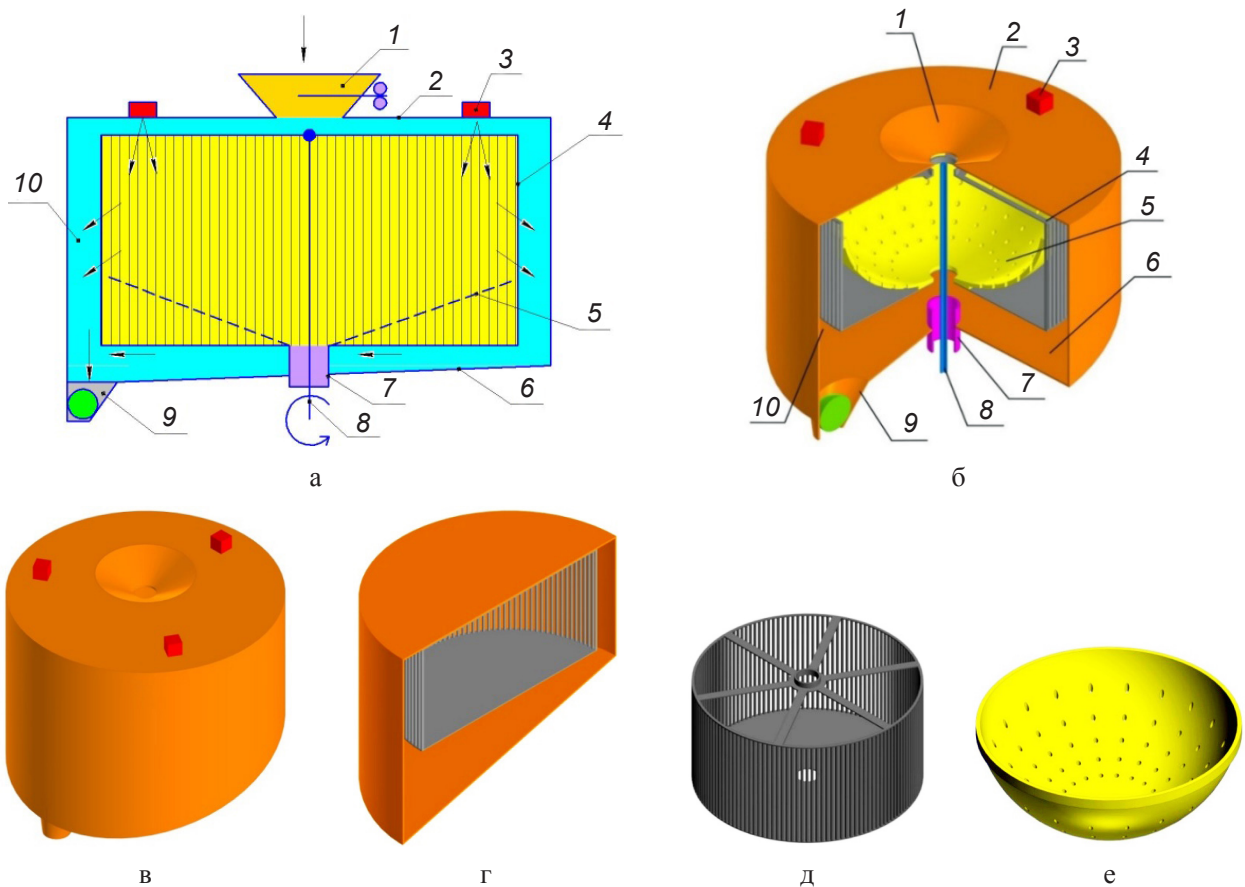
Установка с СВЧ-энергоподводом в щелевой цилиндрический резонатор для вытопки жира из слизистых субпродуктов: а – технологическая схема; б – общий вид; в – расположение магнетронов на корпусе; г – расположение резонатора в корпусе, разрез; д – резонатор; е – керамическая воронка
